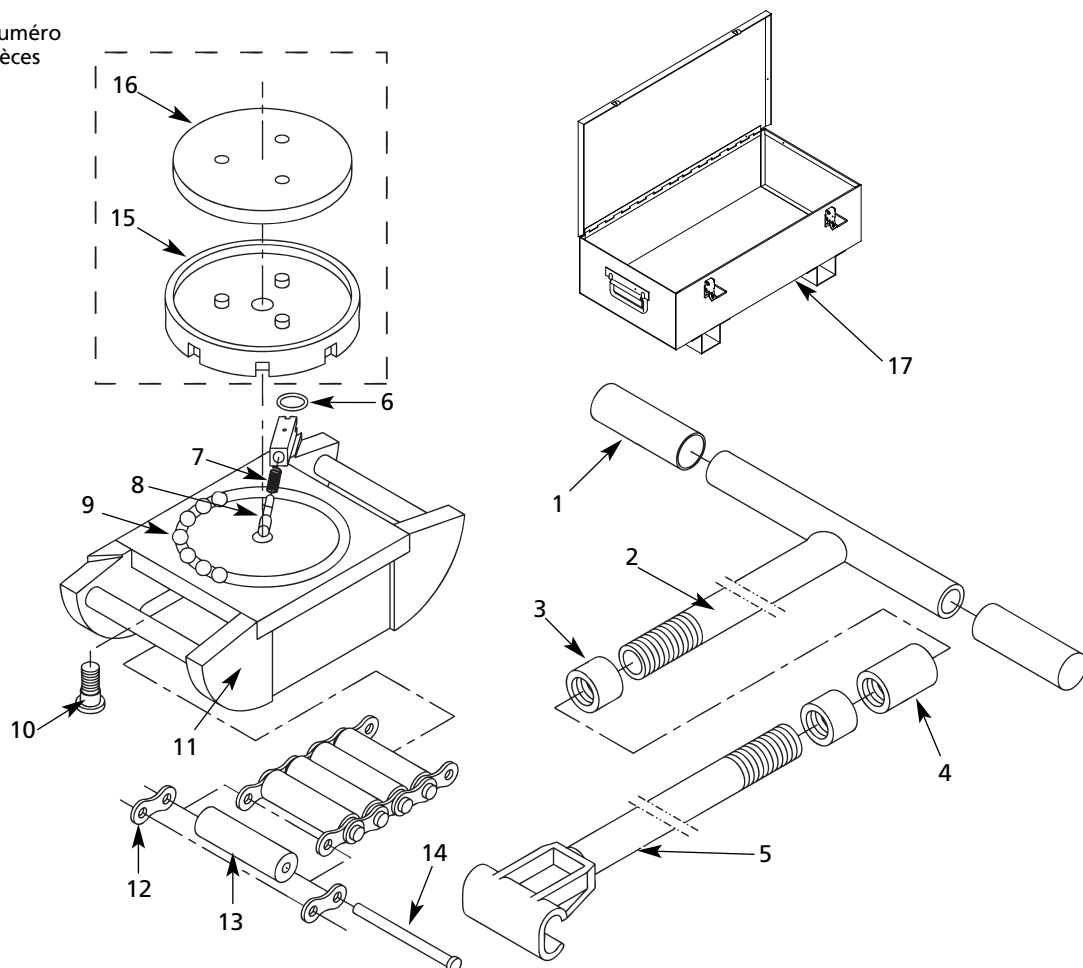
Illustration des pièces détachées pour le 2MPR3
